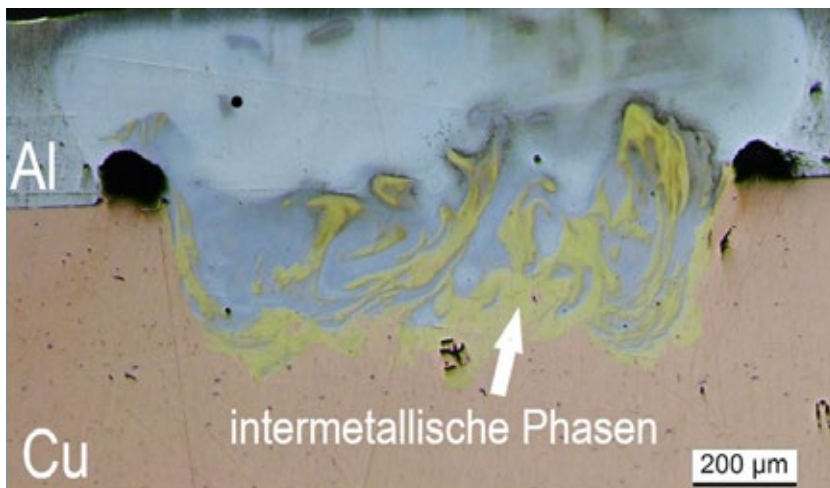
intermetallische Phasen in einer Aluminium-Kupfer-Schweißnaht
